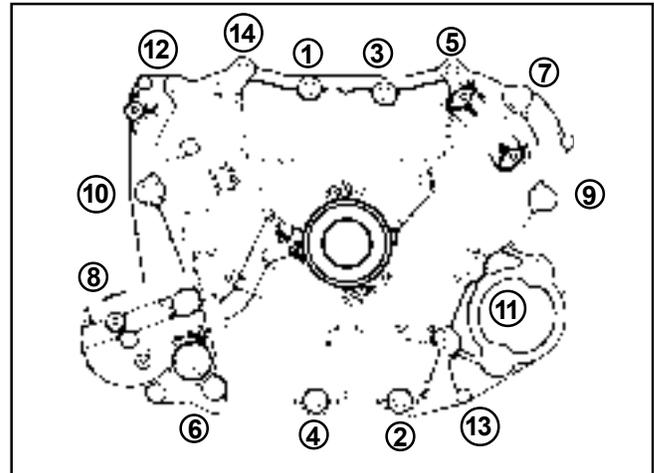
Séquence de serrage des fixations de la plaque de fermeture.
